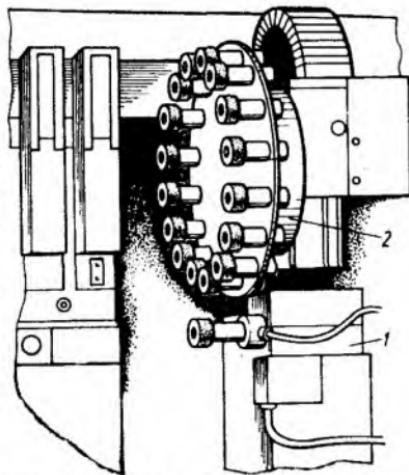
Шлифовальный модуль для внутришлифовального станка с инструментальным магазином:
